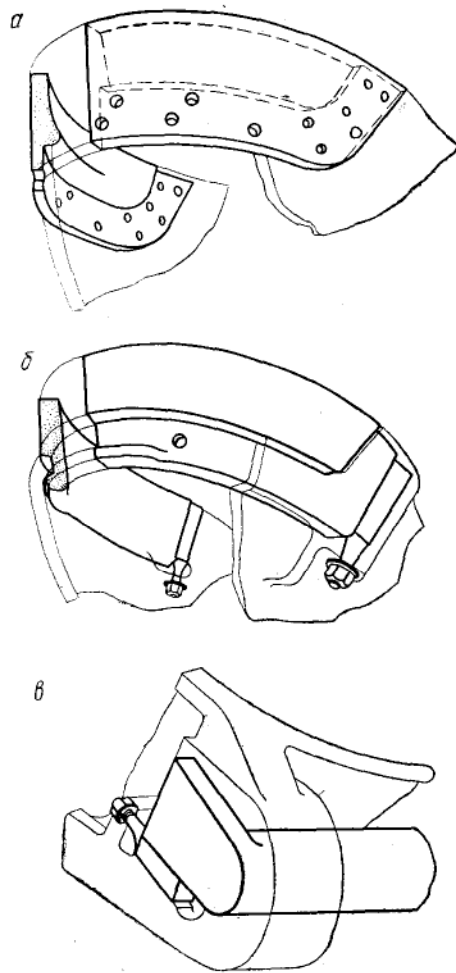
Элементы крепления съемных козырьков и черпачового пальца с конической лапой к корпусу черпака:
